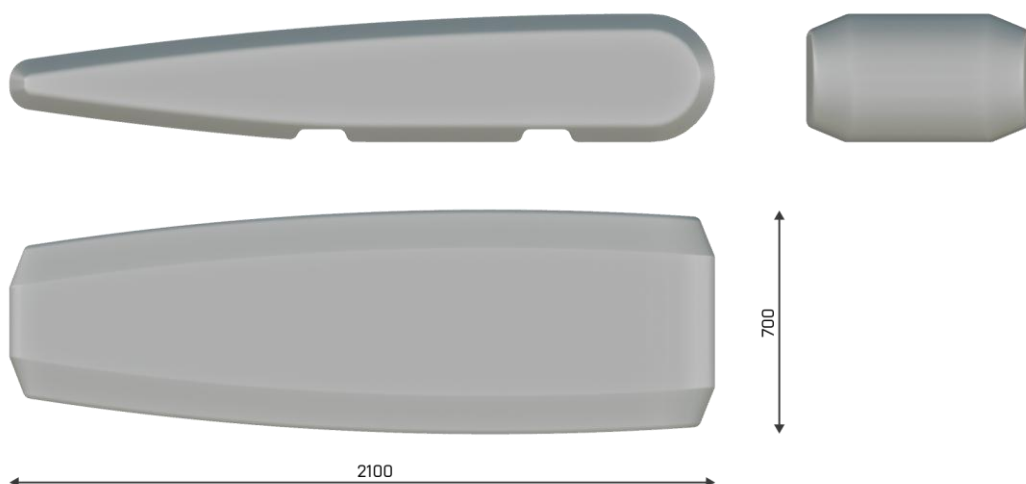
Ilustrační skica předcházející finálním variantám.
